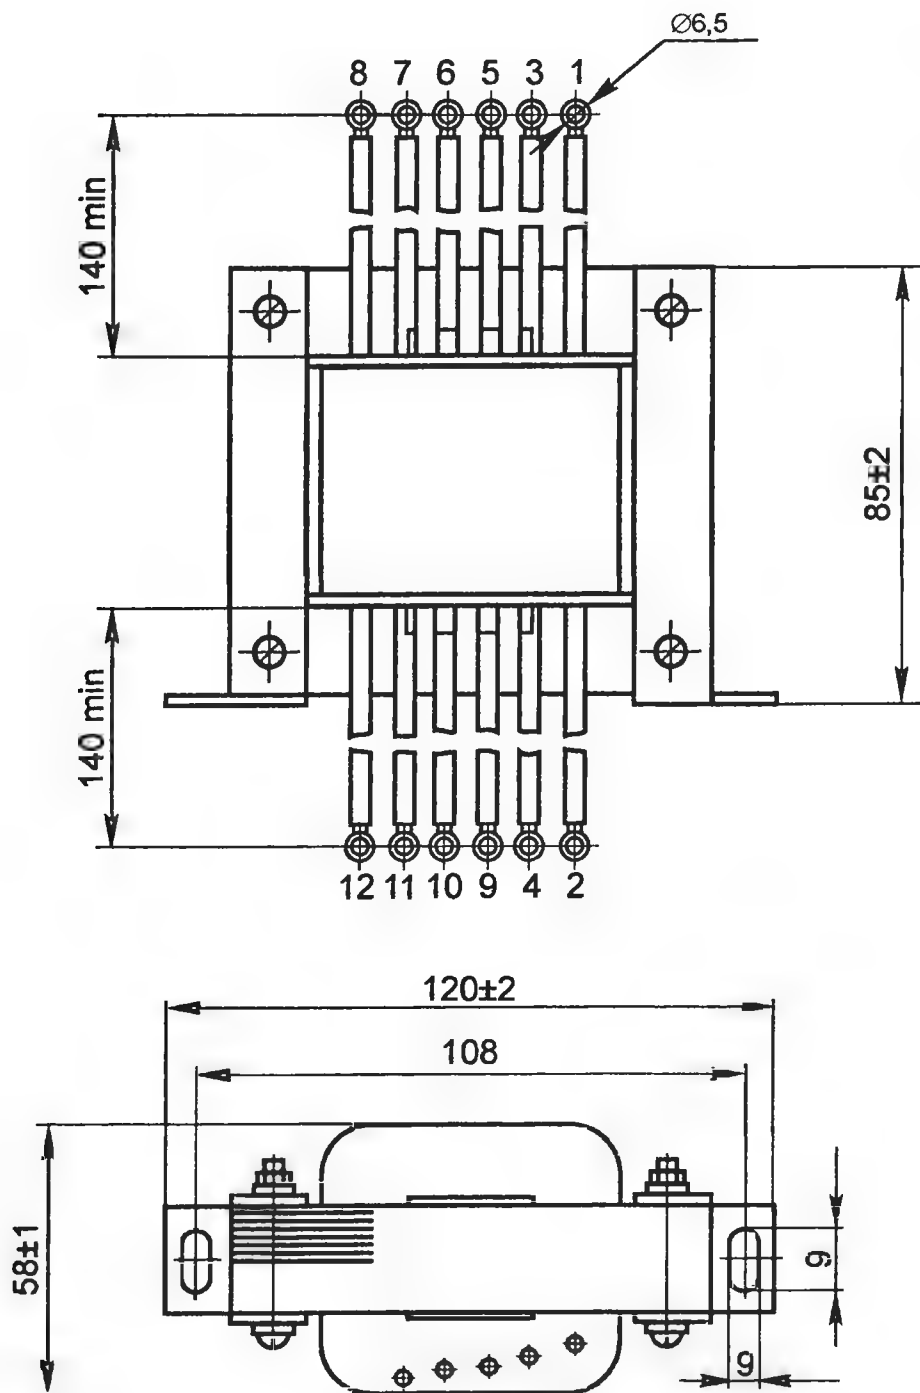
Габаритные и присоединительные размеры трансформаторов СТ-3С и СТ-3СП
